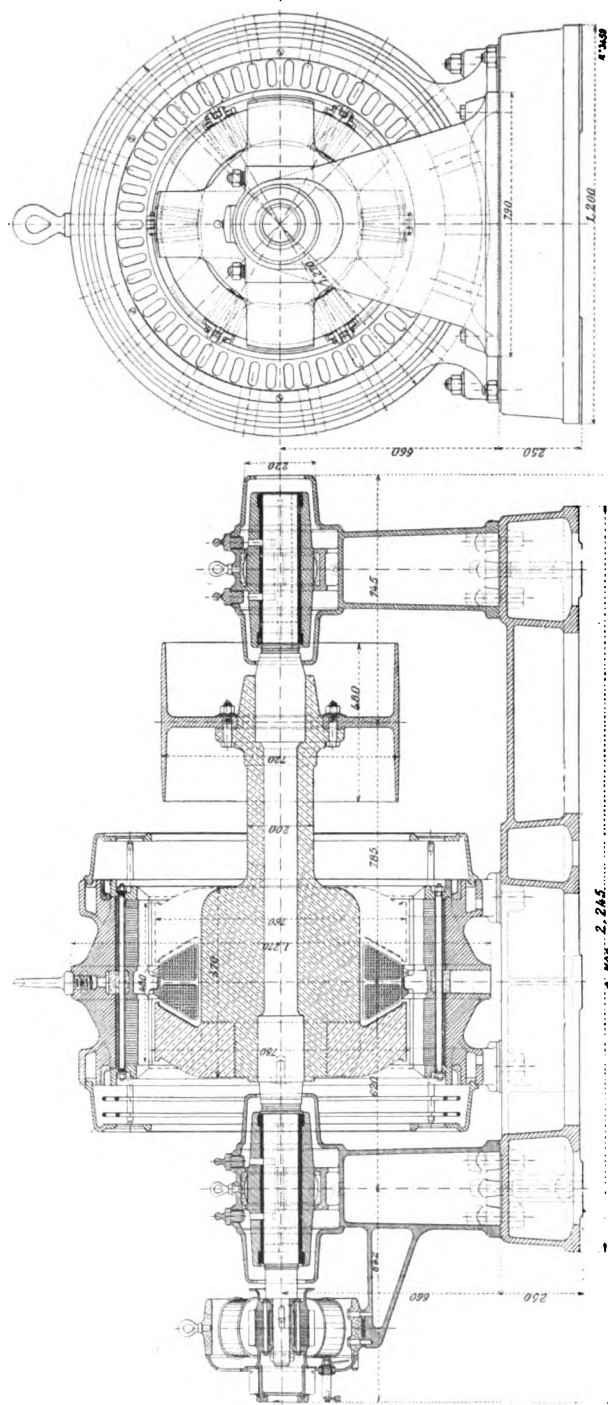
et 2. — Vues d'ensemble avec coupes partielles de l'alternateur à fer tournant de 122 kilovolts-ampères de MM. Siemens et Halske de Vienne.
